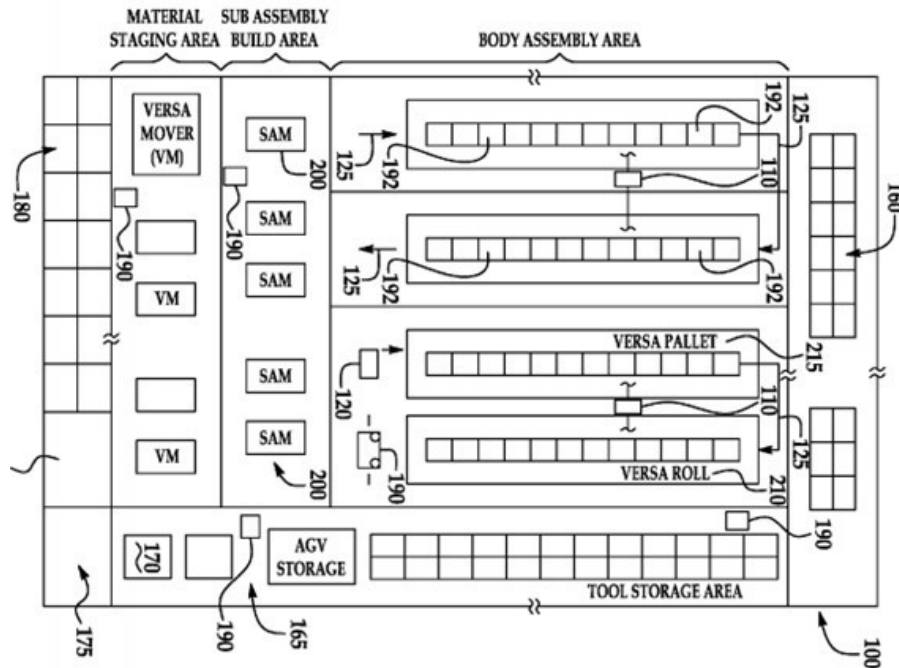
Ejemplo de planta modular con estaciones de servicio (Kilibarda et al., 2014)
